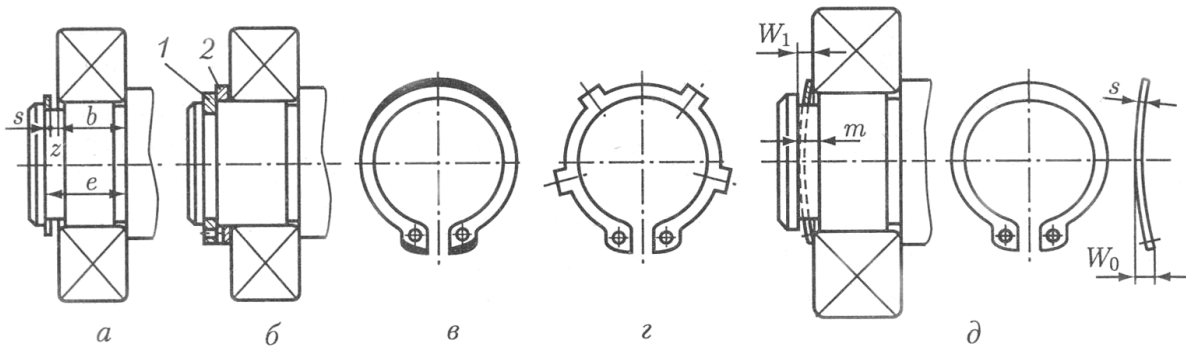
Крепление подшипников на валах пружинным упорным плоским кольцом:
